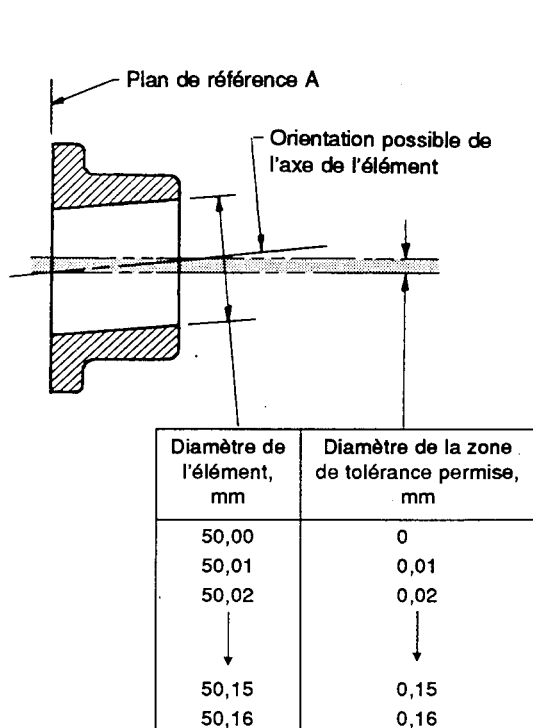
Spécification de la perpendicularité d'un axe ; frontière admissible (goupille ou bossage à l'état au maximum de matière)
